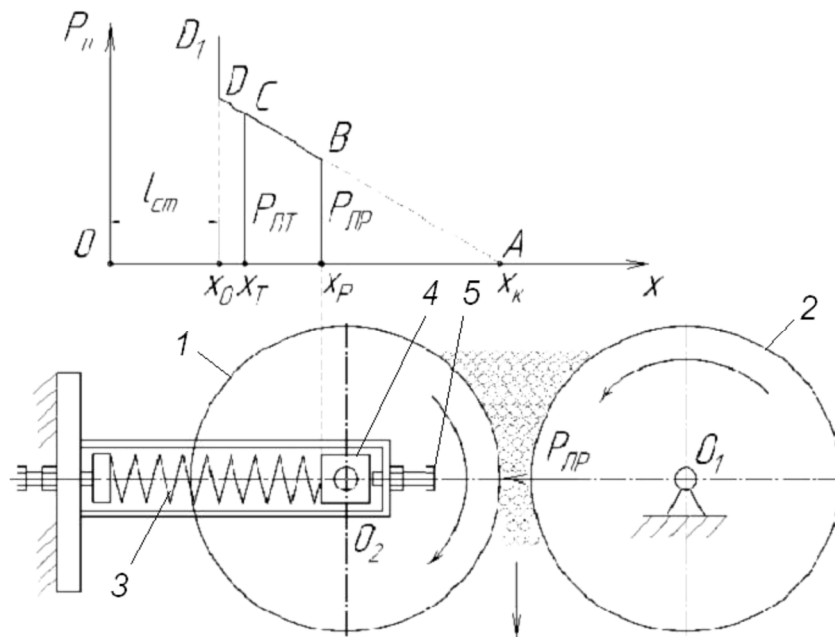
Схема до розрахунку пружин теркового вальцевого апарата і визначення їх жорсткості: 1 – притискний валець; 2 – опорний валець; 3 – пружина; 4 – підшипник притискного вальця; 5 – регулювальний болт
